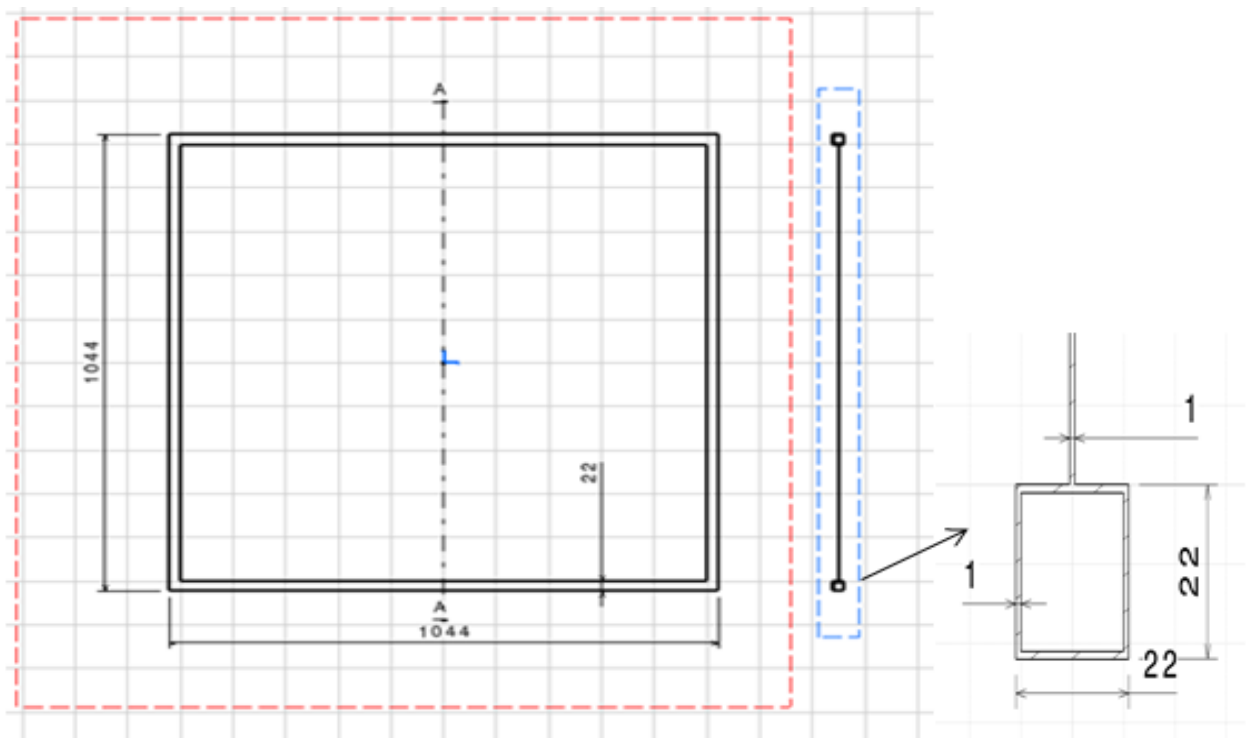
Desenho da Placa com reforço quadrado oco de 1 mm
